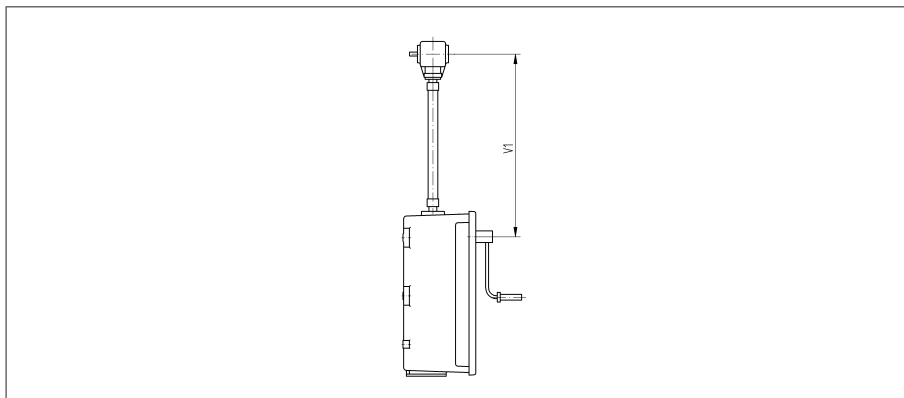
Приводной вал без шарнирного вала и изолятора (стандартное исполнение)
